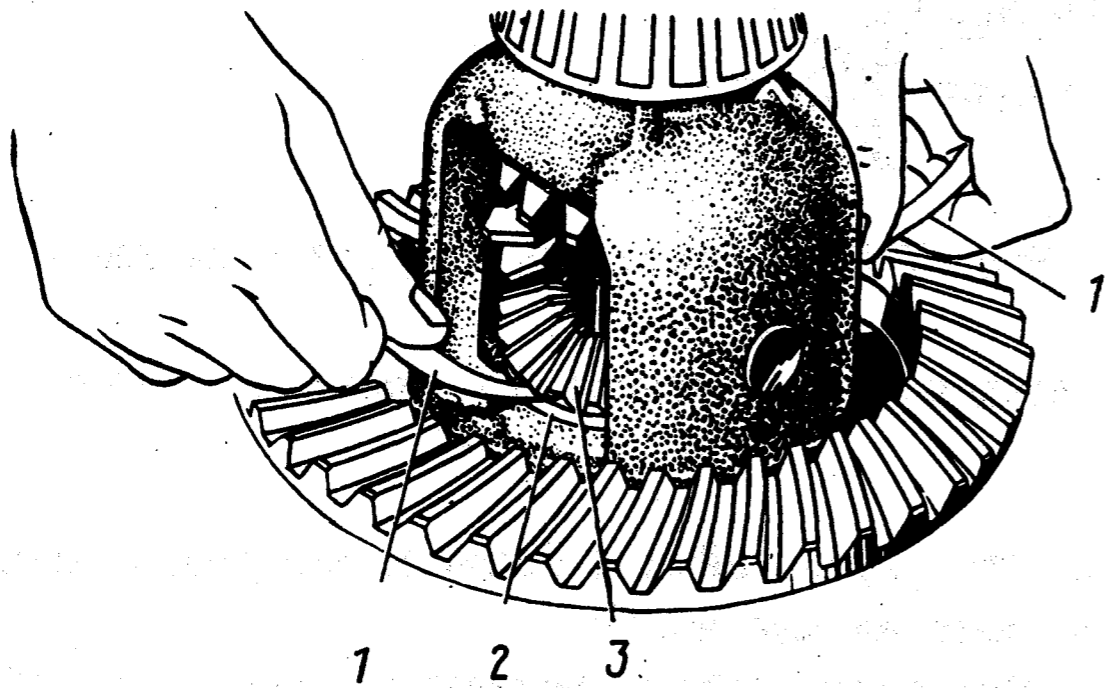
Проверка зазора в дифференциале: 1 - щуп; 2 - шайба упорная; 3 - шестерня
